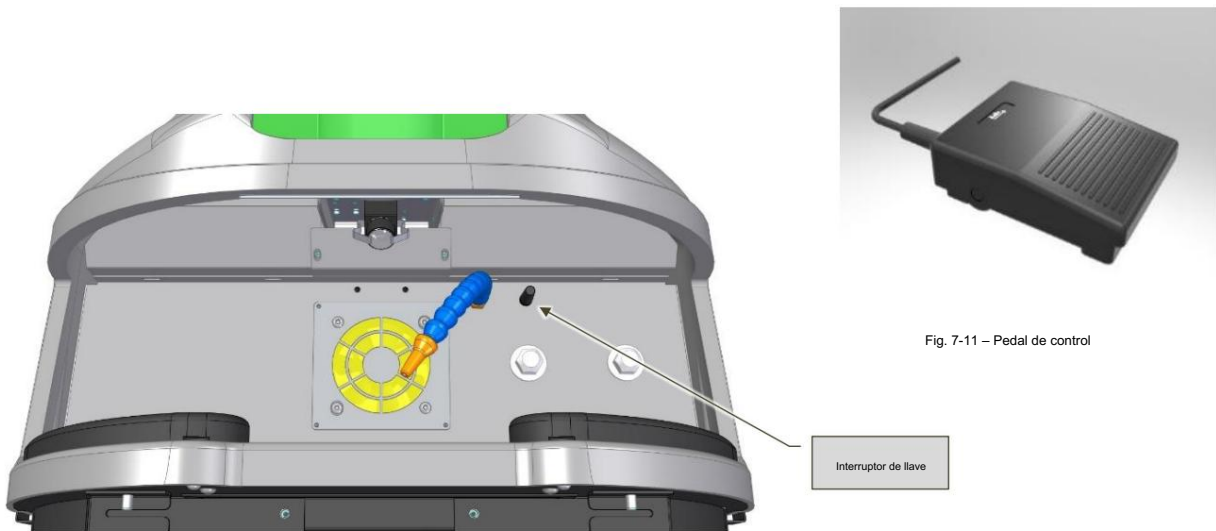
Dispositivos de control dentro de la cámara de soldadura
